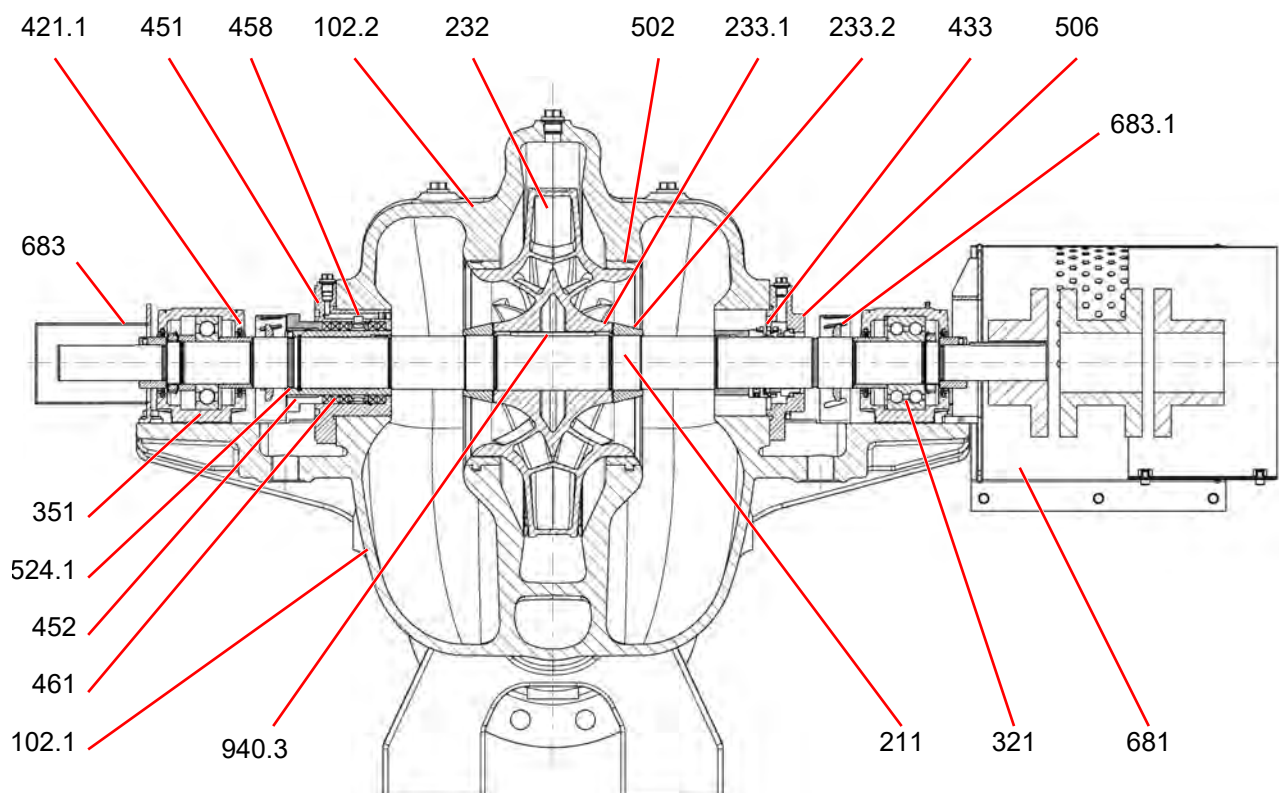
Чертеж насоса ASP-R в разрезе (соосные лопасти рабочего колеса, призматическая шпонка)
